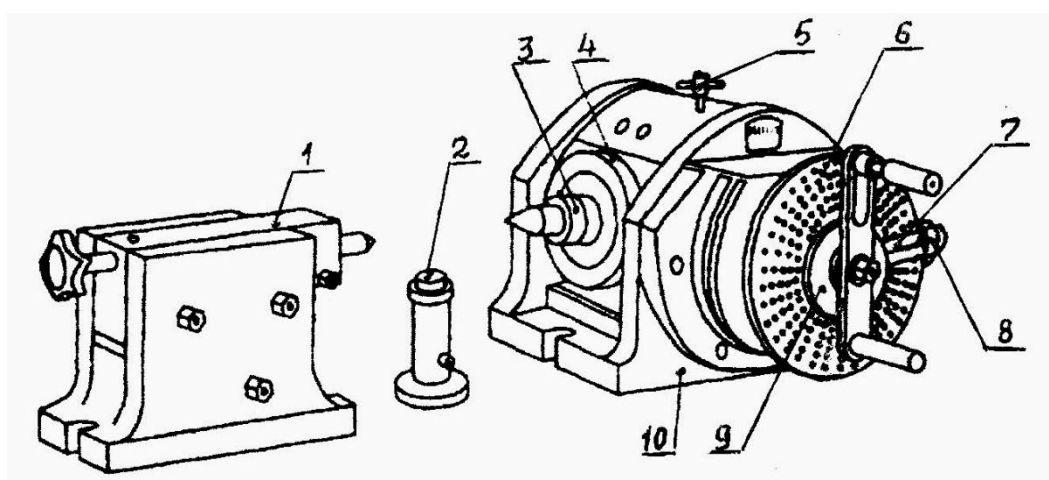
Универсальная делительная головка с задней бабкой и люнетом: 1 – задняя бабка с конусом; 2 – люнет; 3 – поворотная головка со шпинделем и центром; 4 – градусная шкала; 5, 8 – стопоры; 6 – боковой делительный диск; 7 – две линейки; 9 – раздвижной сектор; 10 – корпус
